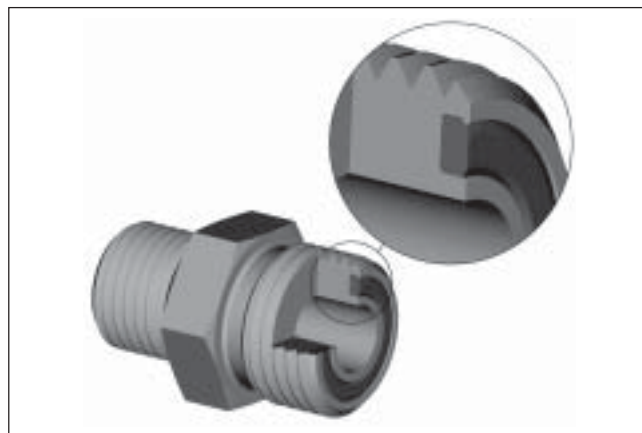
Vista seccionada de la ranura para junta tórica cautiva (CORG)
